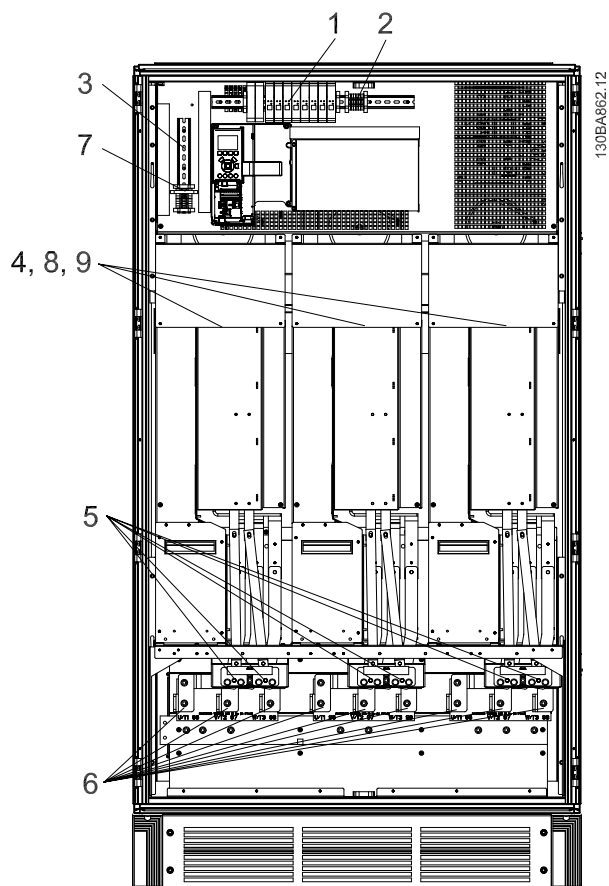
Шкаф инвертора, размер корпуса F2 и F4
